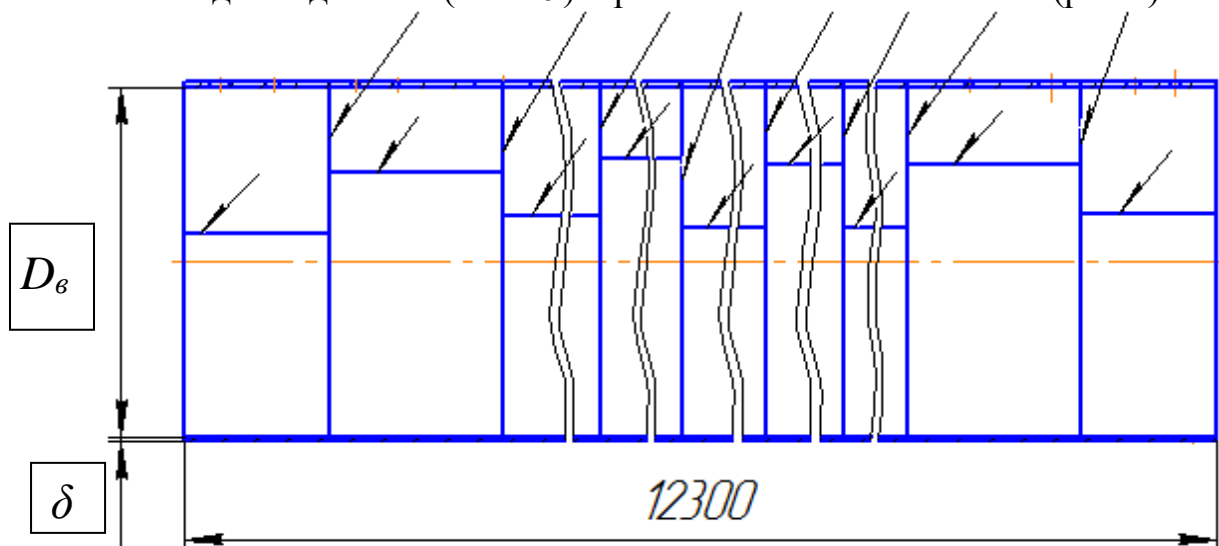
Расчетная схема сварки обечайки.
